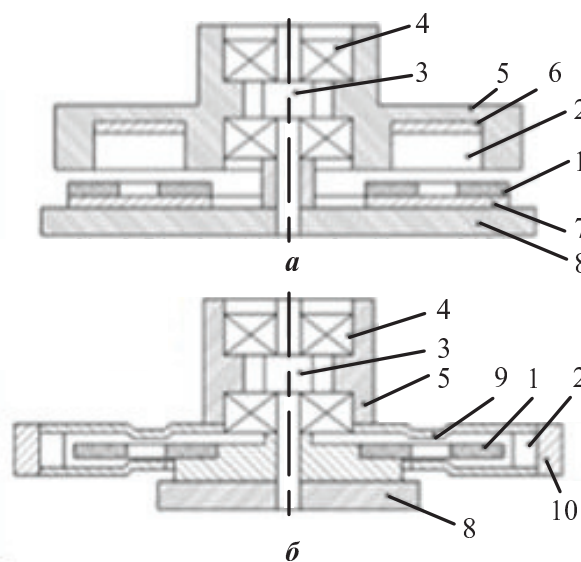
Конструкция дискового привода жесткого диска компьютера: 1 – катушки статора; 2 – ВПМ; 3 – вал; 4 – подшипники; 5 – ступица; 6 – ярмо ротора; 7 – ярмо статора; 8 – основание; 9 – конструкционные изгибы; 10 – немагнитное кольцо
